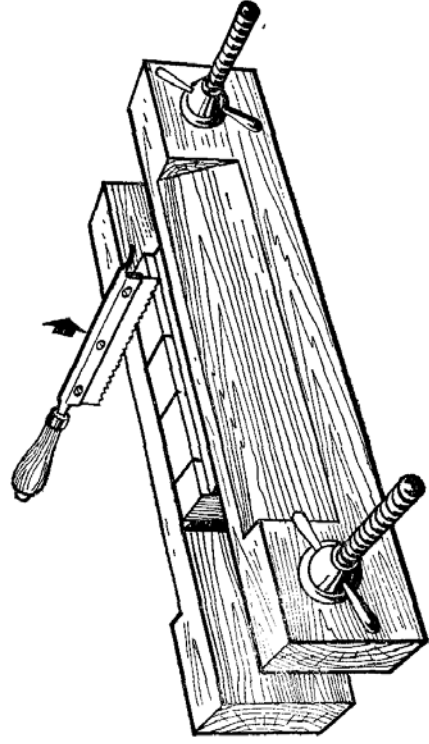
Разметка и пропилка блока, зажатого в тисках
